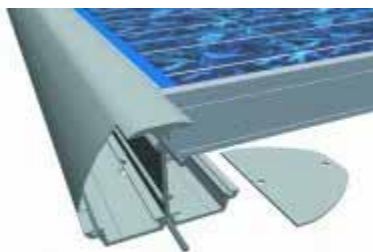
Calha de encaixe e placa terminal para as secções Sol-50
